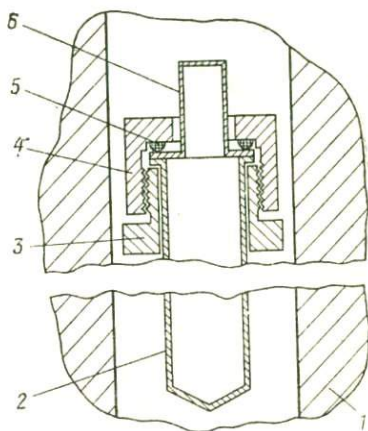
Затвор для плавающего фторопластового вкладыша:
